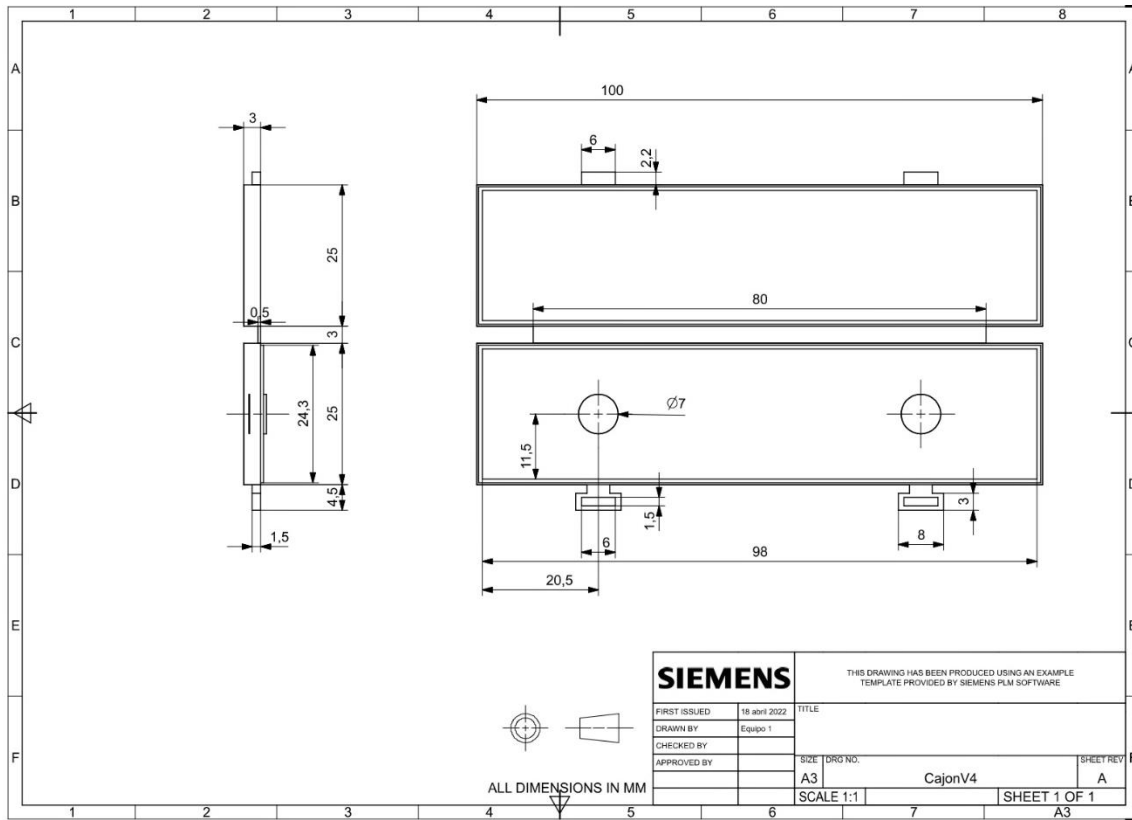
Plano de diseño de Carcasa "Sensor Shield"
